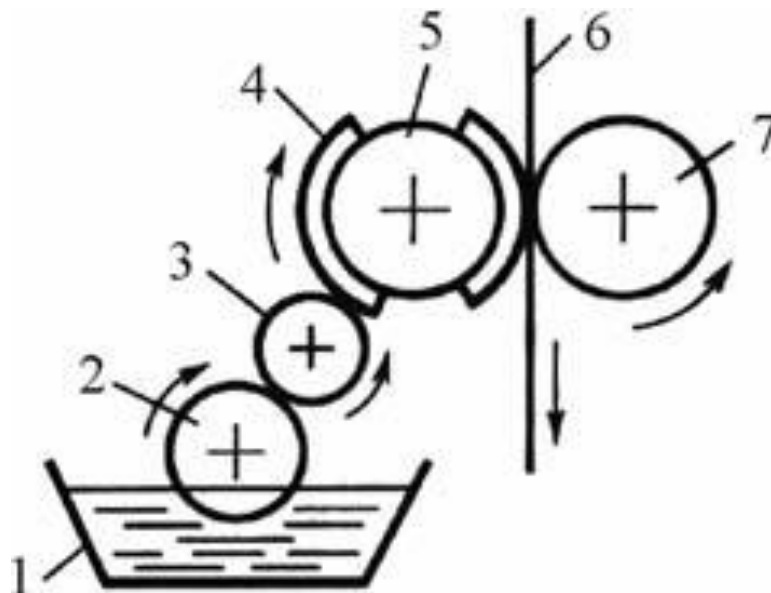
Схема друкарського апарату флексографської машини: 1 – барвистий резервуар; 2 – дукторний вал; 3 – передавальний валик; 4 – друкована форма; 5 – формний циліндр; 6 – матеріал, що запечатується; 7 – друкарський циліндр
